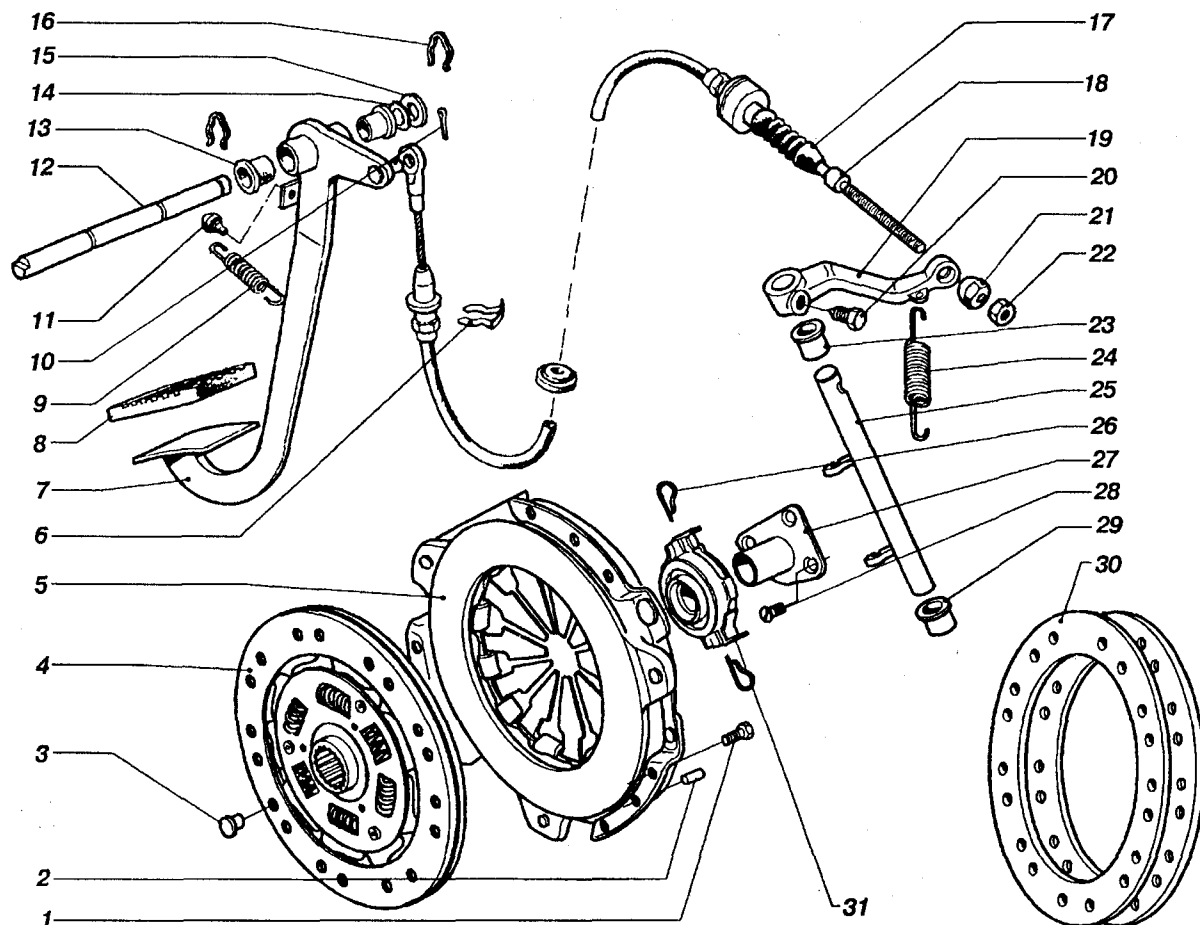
Детали механизма сцепления и его привода: 1 – болт; 2 – штифт; 3 – заклёпка; 4 – диск ведомый; 5 – диск нажимной; 6 – скоба; 7 – педаль сцепления; 8 – накладка педали; 9 – пружина; 10 – шплинт; 11 – упор педали сцепления; 12 – ось; 13 – втулка; 14 – фиксатор; 15 – упор фиксатора; 16 – защёлка; 17 – чехол троса; 18 – трос сцепления в сборе; 19 – рычаг; 20 – стопор; 21 – сухарь; 22 – гайка; 23 – втулка; 24 – пружина; 25 – вилка; 26 – звено соединительное; 27 – фланец; 28 – винт; 29 – втулка; 30 – фрикционная накладка; 31 – выжимной подшипник (6-520806K1E1)
